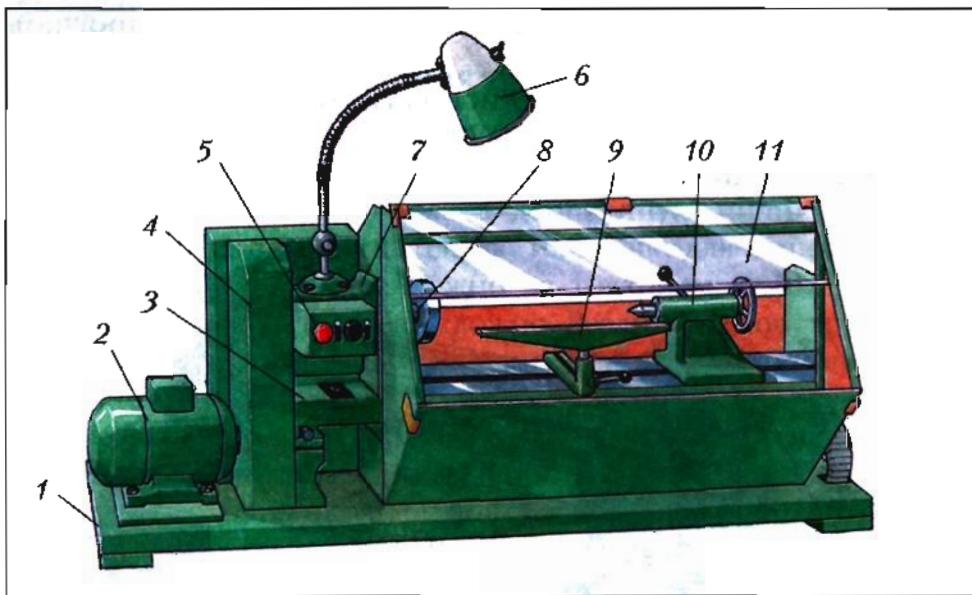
Токарный станок СТД-120 М для точения древесины:
